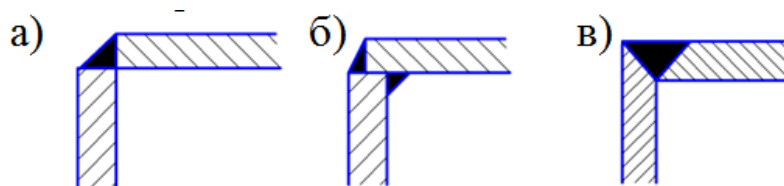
Угловые сварные соединения: а) односторонние без подготовки кромок; б) двухсторонние без подготовки кромок; в) односторонние с подготовкой кромок.
